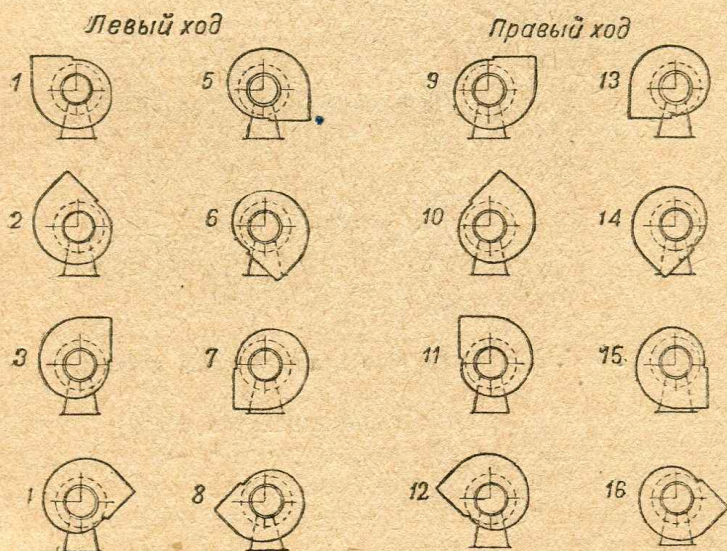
Крепление поворотного кожуха вентилятора к станине
